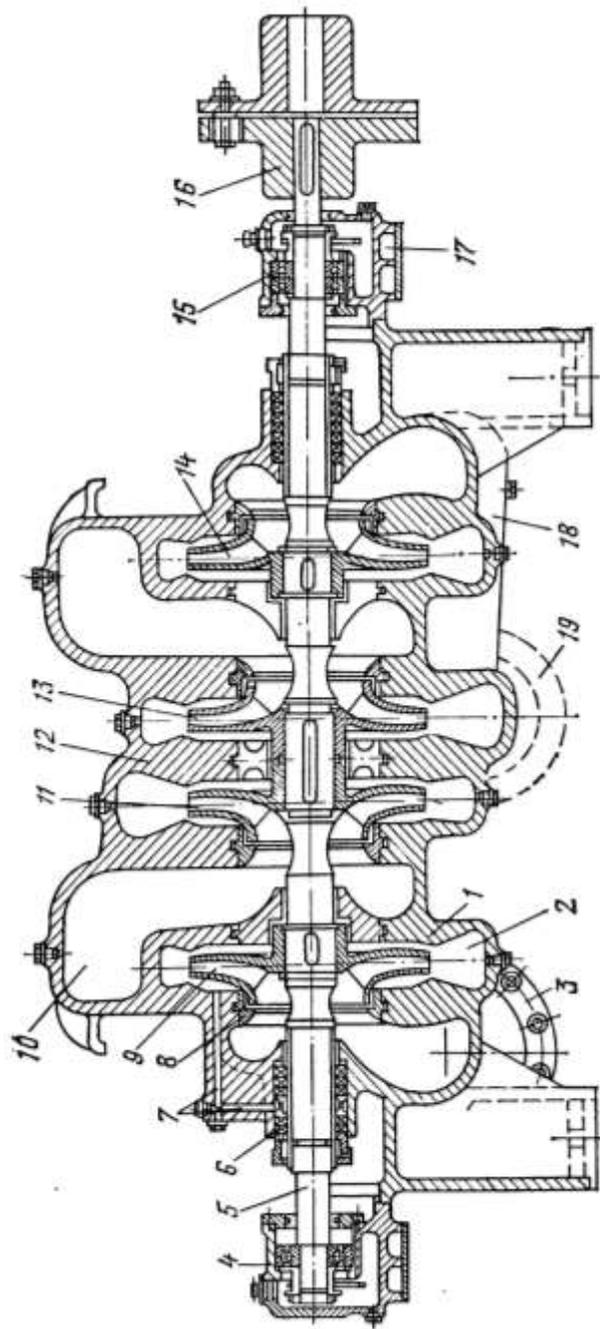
Конструкция центробежного четырехступенчатого насоса с горизонтальным разъемом корпуса:
